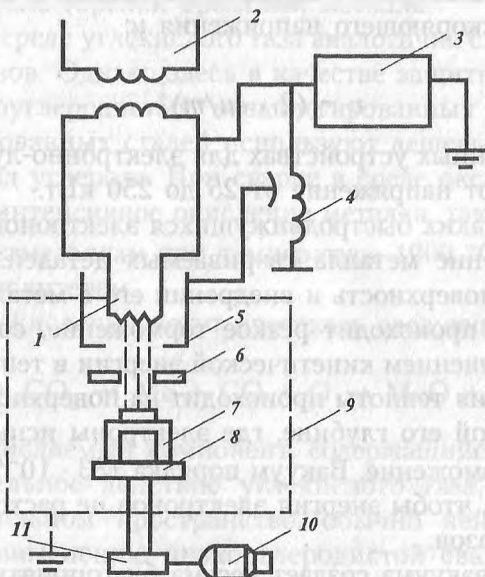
Схема установки для сварки электронным лучом
